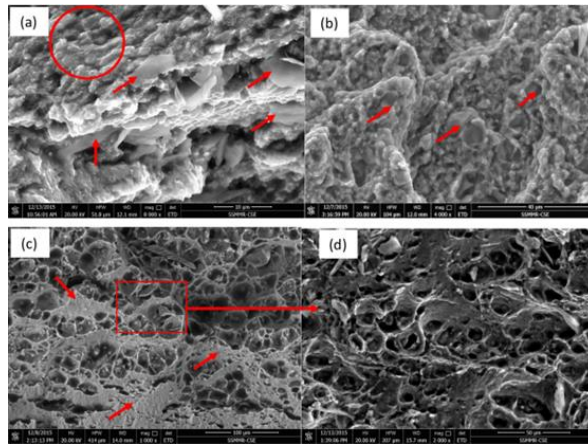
10 mm kalınlığındaki Al 7075-T651 levhasının elektron mikroskopu resimleri a.Ana malzeme b.Kaynak metali bölgesi,c. Termomekanik etkilenen bölge d.ısı ile etkilenen bölge d.ısı ile etkilenen bölge [9].
